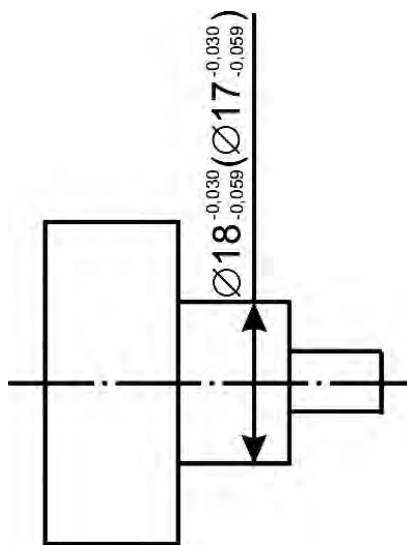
Обозначение допустимых без ремонта размеров и допусков
